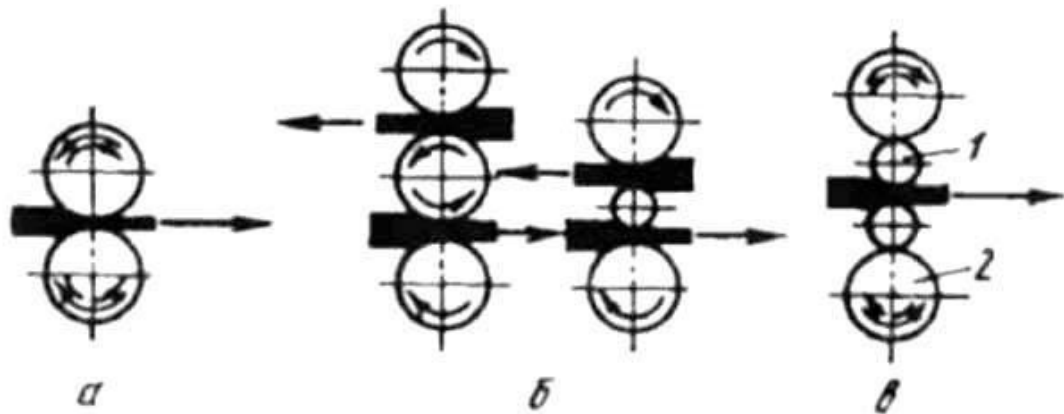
Схеми розташування прокатних валків: а – двовалкова прокатна кліть (дуо); б – тривалкова (тріо); в – чотиривалкова прокатна кліть
